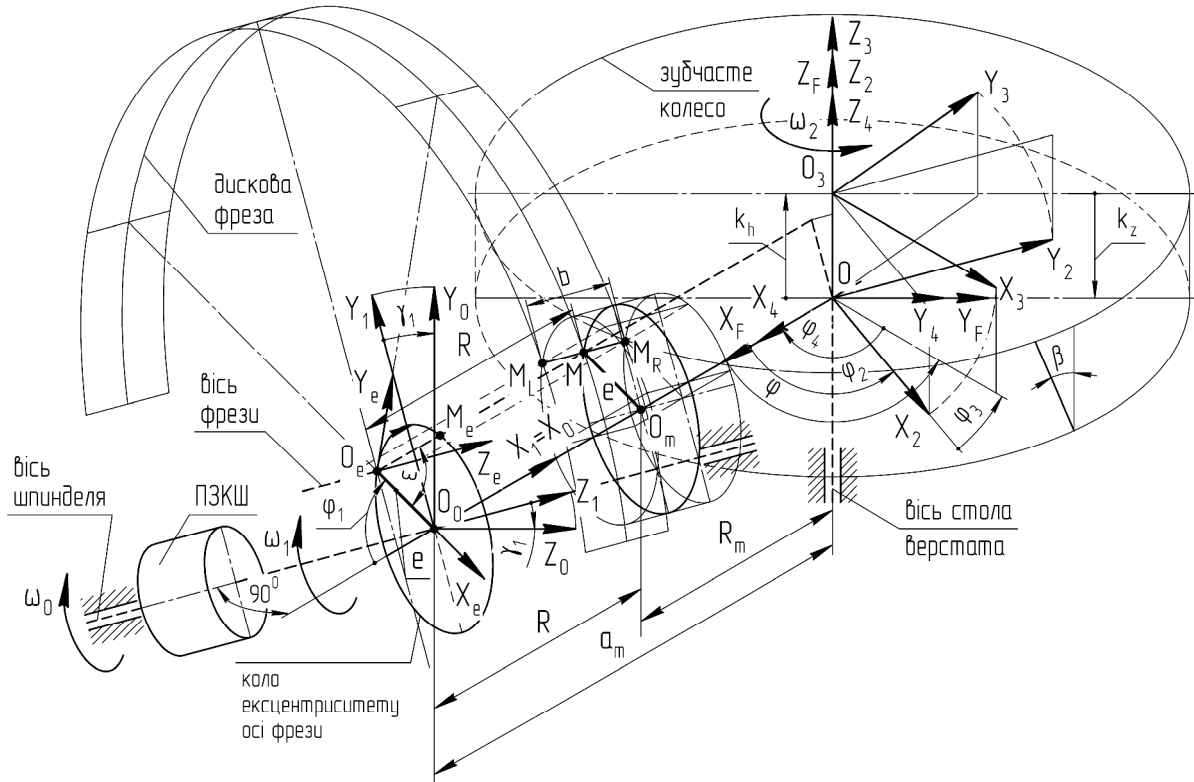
Формування бокових поверхнь зубців циліндричних косозубих коліс дисковою фрезою способом радіально-колового кінематично змінюваного формоутворення
